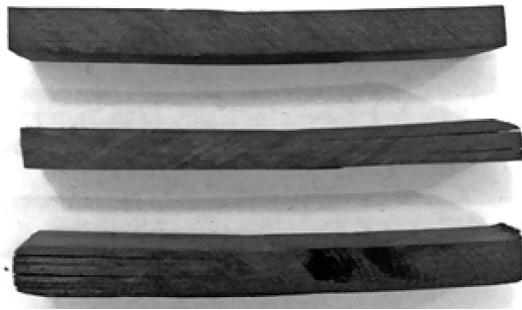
Образец углепластика, изготовленный с применением ИК нагрева (после испытаний)
